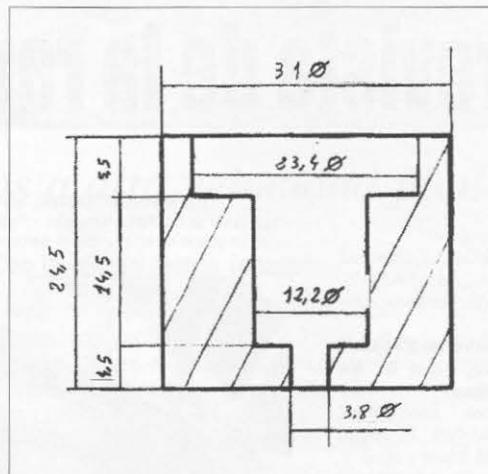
Pieza aislante, en nilón, que irá insertada a ajuste duro, en el interior del cuerpo de aluminio del conector adaptador.
